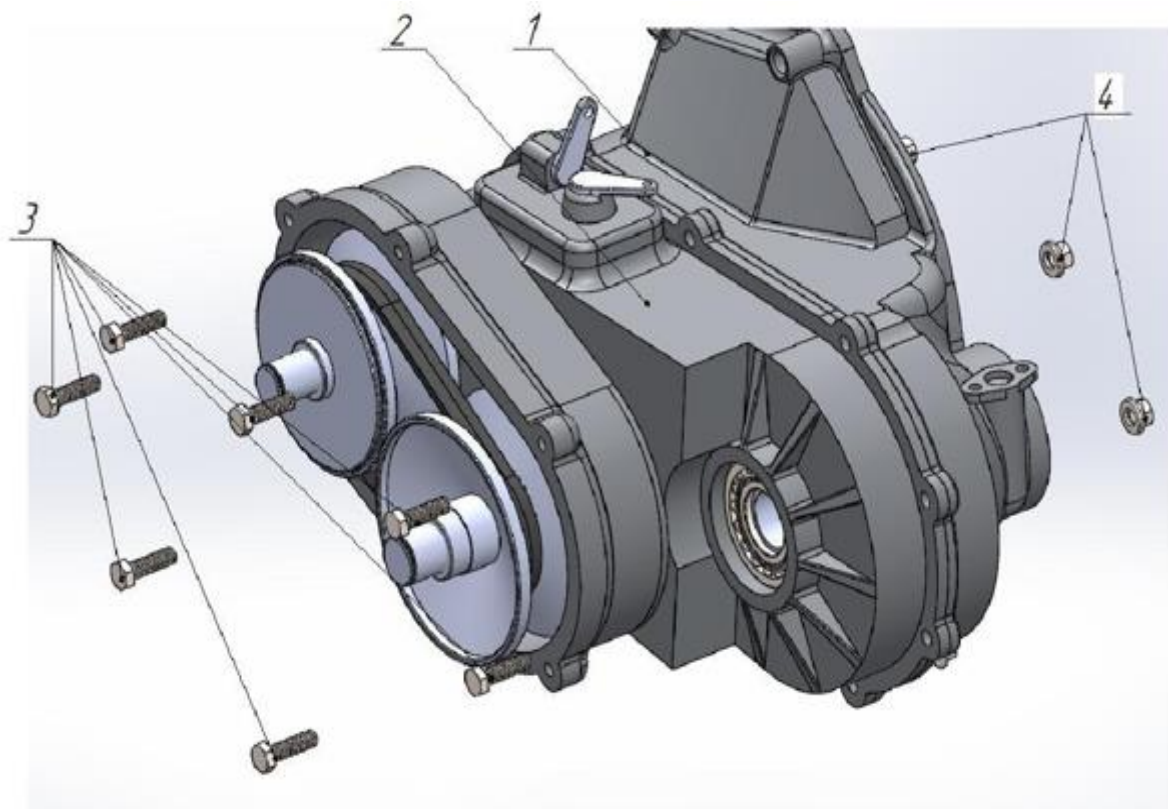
Бесступенчатая коробка передач: 1 – крышка коробки передач; 2 – корпус; 3 – крепежные болты; 4 – гайки
